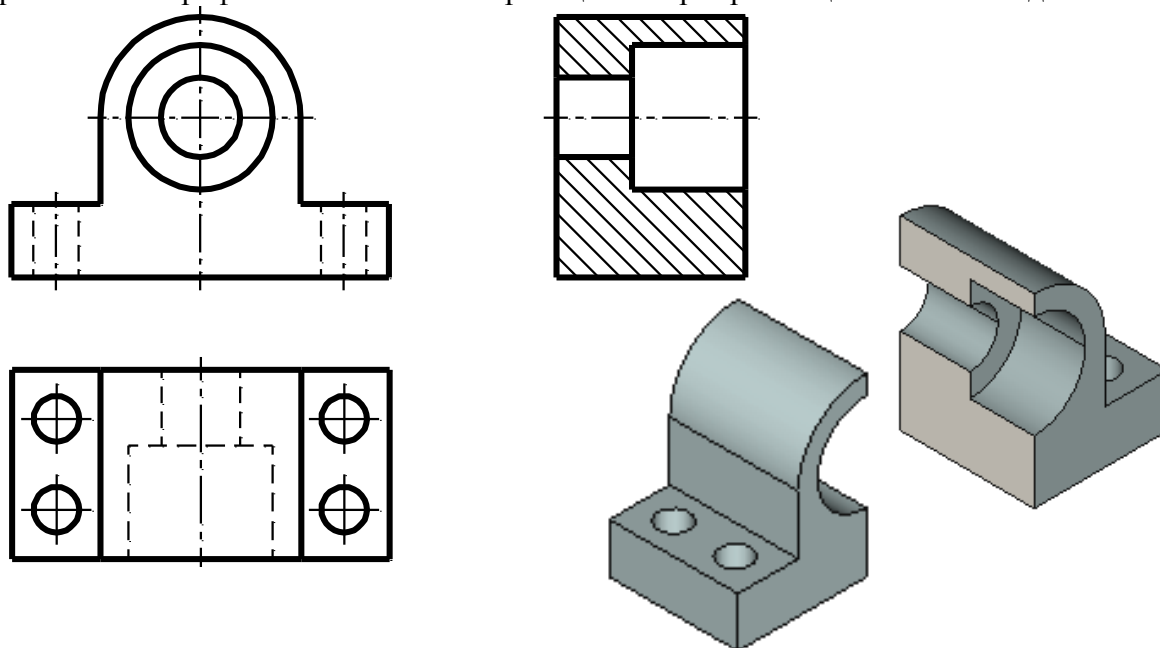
Главный вид, вид сверху и профильный разрез
